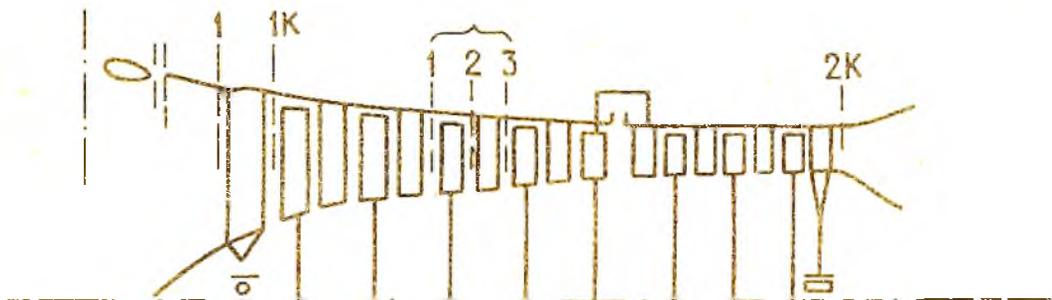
Схема и условные обозначения сечений проточной части осевого компрессора
